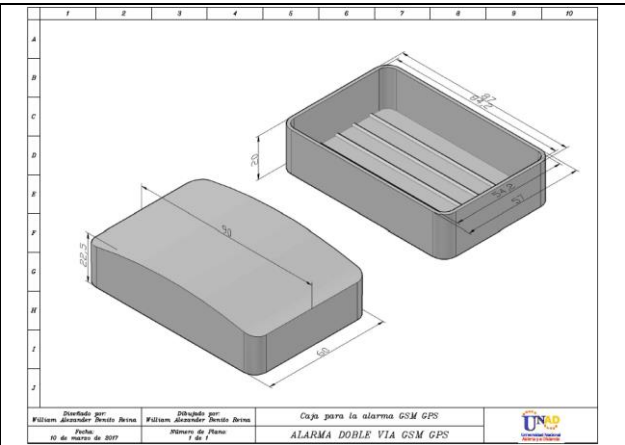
Plano de la caja de la alarma realizado en AutoCAD 2015
